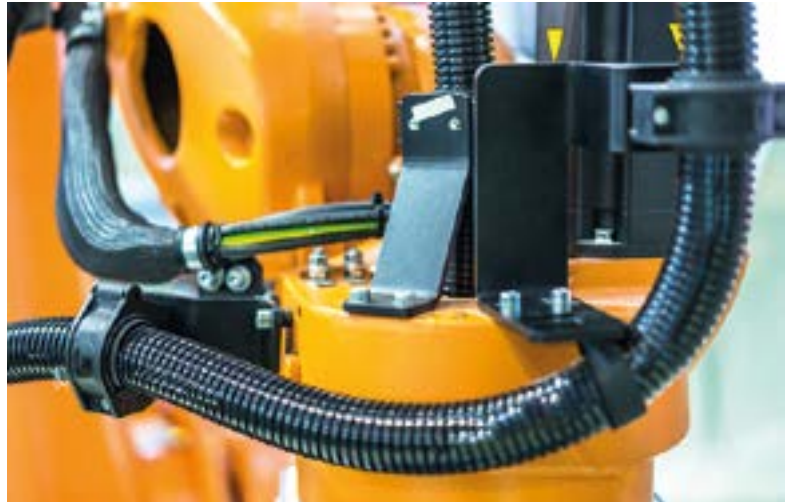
El paquete de protección de cables es un método más avanzado y emplea tubos de plástico corrugado como alojamiento adicional (fuente: THINK b/stock.adobe.com).
